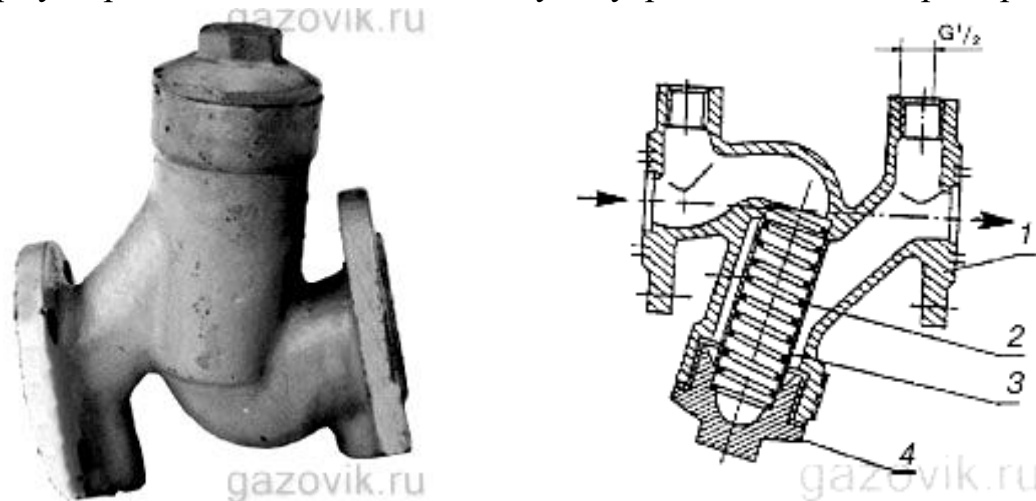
Фильтр сетчатый типа ФС: 1 — корпус; 2 — кассета; 3 — сетка; 4 — пробка
